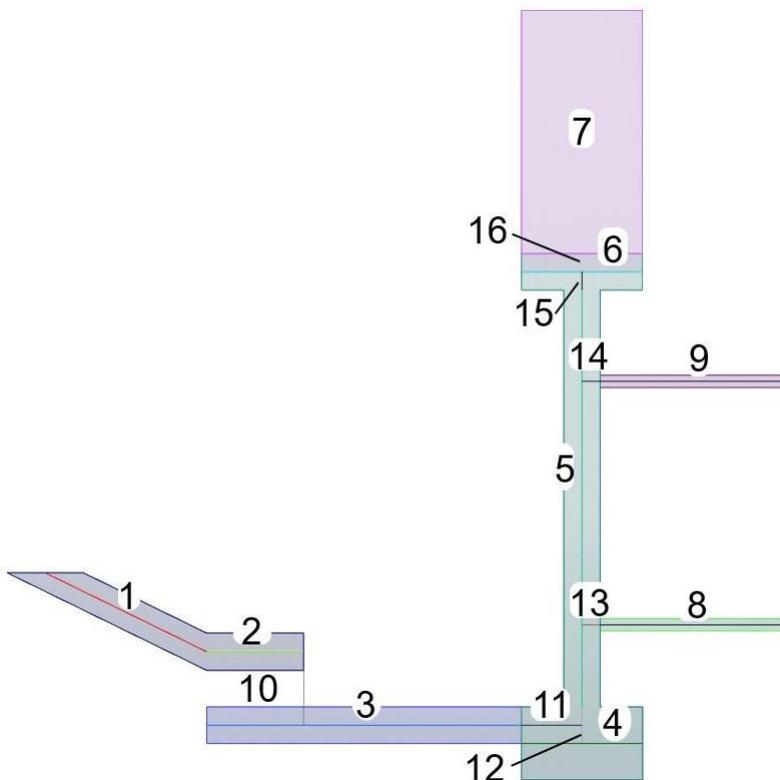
3D-профили оболочечной модели со стороны компрессора
